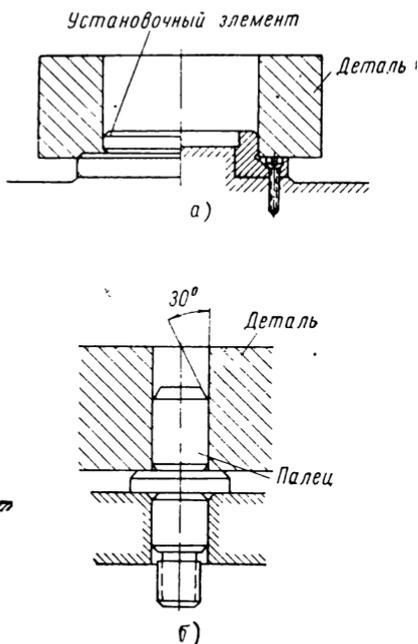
Схема установки детали: а — по установочному цилиндрическому элементу, б — по пальцу
